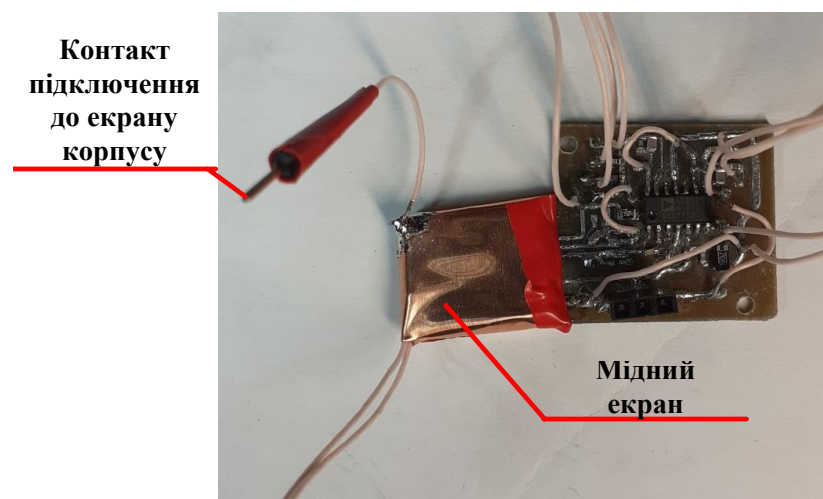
Додатковий мідний екран, який покриває інструментальний підсилювач
